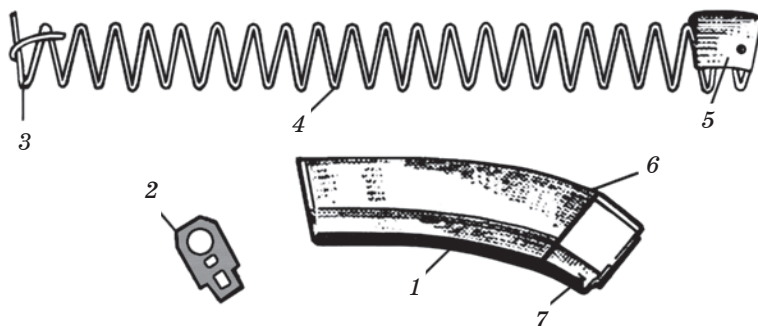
Магазин: 1 — корпус; 2 — крышка; 3 — стопорная планка; 4 — пружина; 5 — подаватель; 6 — опорный выступ; 7 — зацеп
